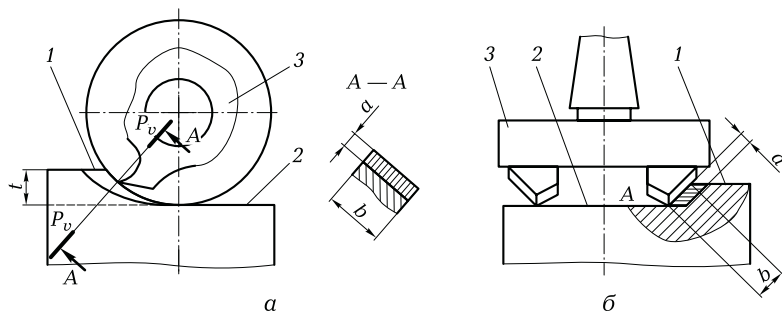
Сечения срезаемых слоев при фрезеровании цилиндрической (а) и торцевой фрезой (б) с вставными ножами:
